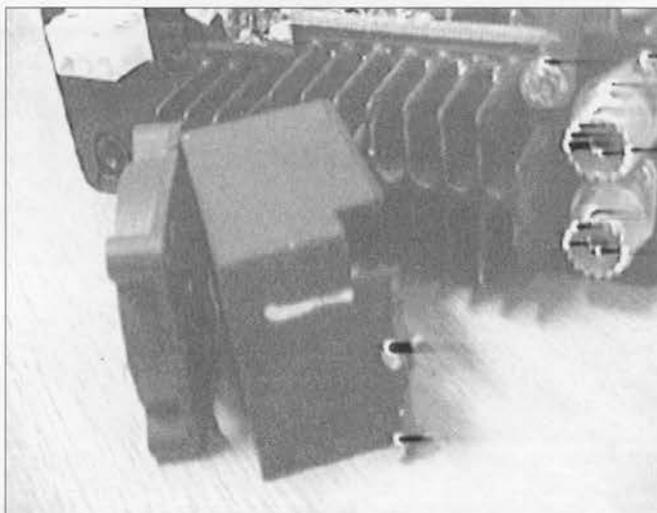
El pequeño rebaje que tiene la pieza adicional de duraluminio en su parte superior derecha es para salvar el tornillo de la conexión de tierra del equipo.
